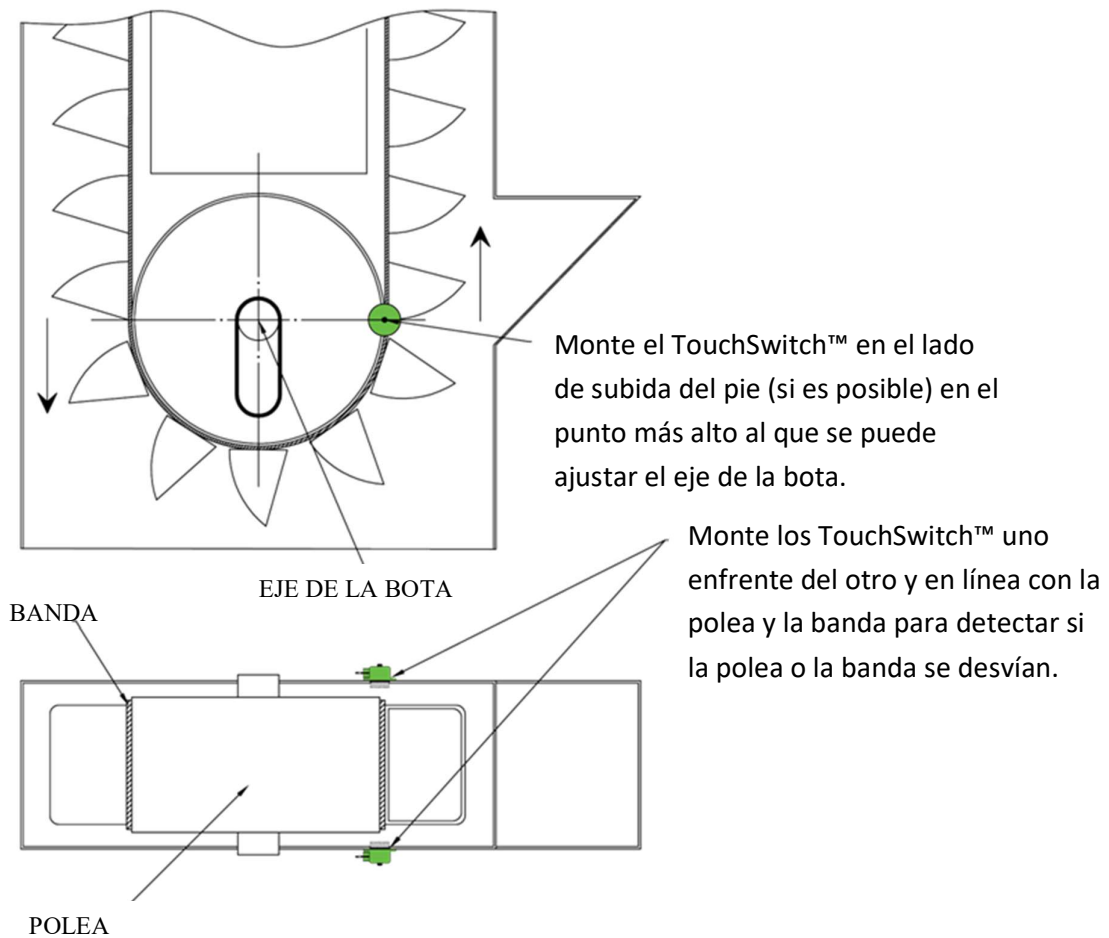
Posiciones de montaje del TouchSwitch™ – Pie de elevador
